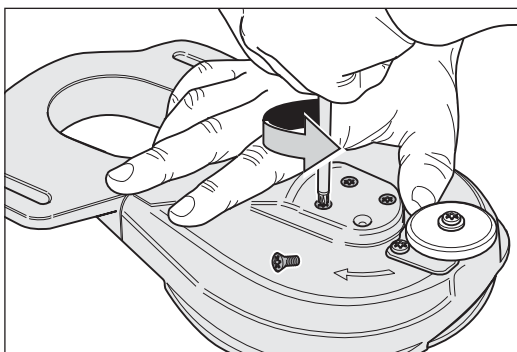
Die vier Befestigungsschrauben des kompletten Schleiftellers entfernen.
